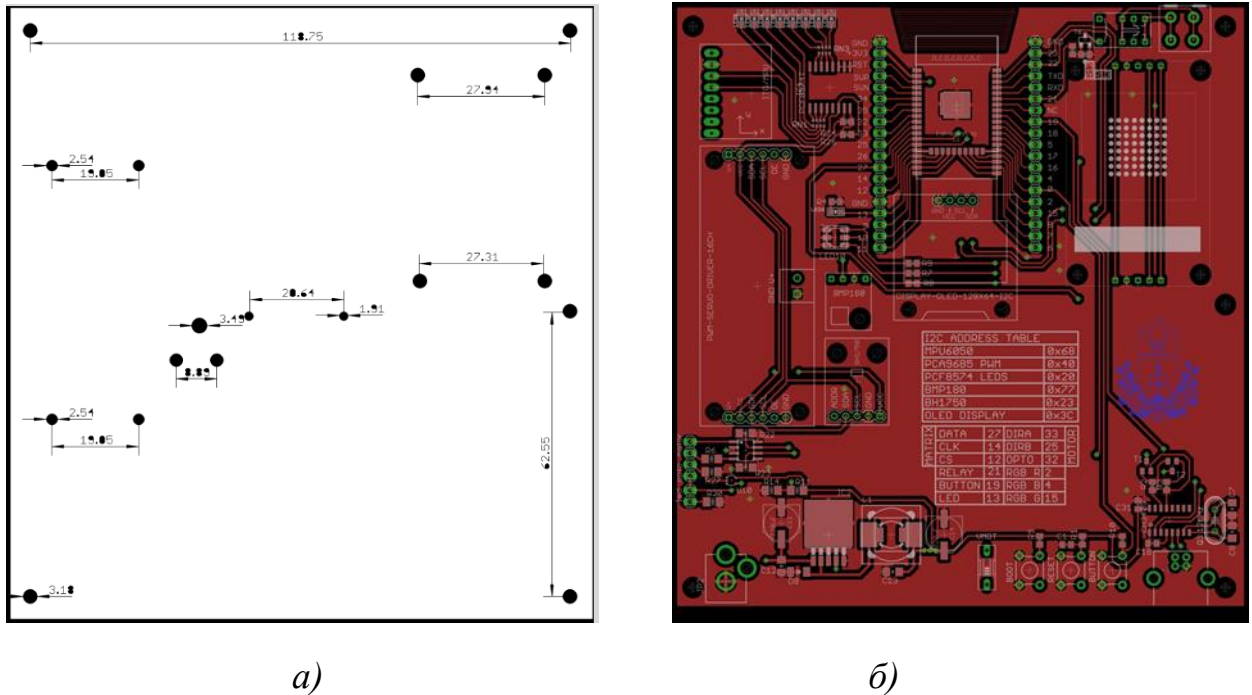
Схема монтажно́ї плати: а) монтажне креслення, б) верхній шар друкованої плати
